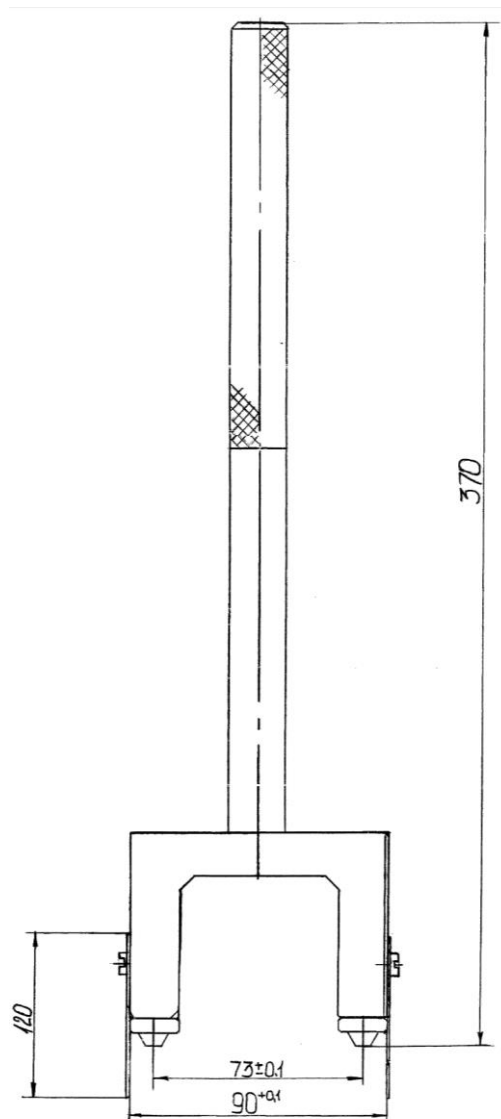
ЗМ 7823-4731, Оправка для демонтажа шатунно-поршневого комплекта из цилиндра
